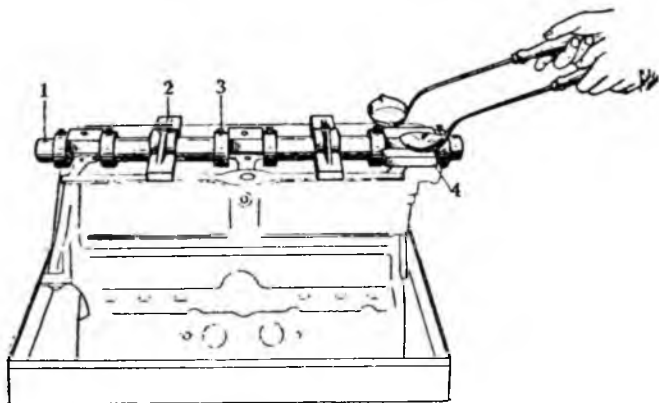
Прибор для заливки коренных подшипников в блоках автомобиля ГАЗ (в рабочем положении):
